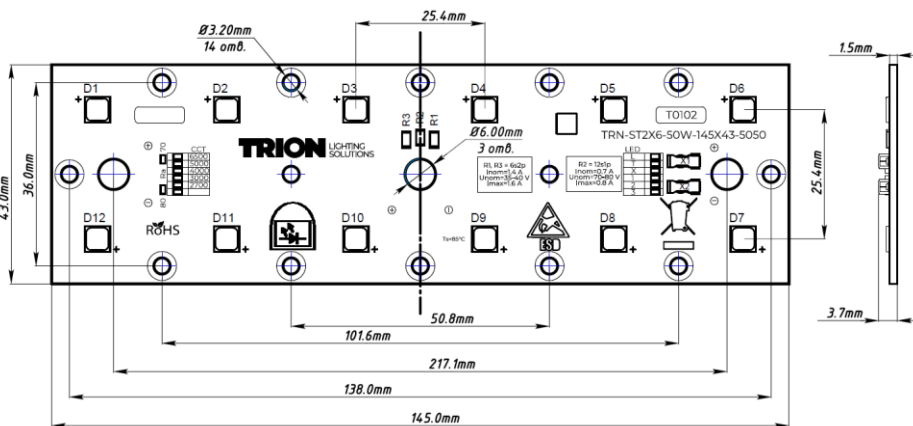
Внешний вид с габаритными и присоединительными размерами изделия (TRN-ST2X6-50W-143X44-5050)
